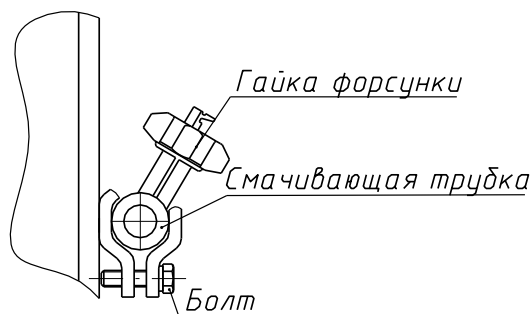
Регулировка направления потока смачивающей жидкости
